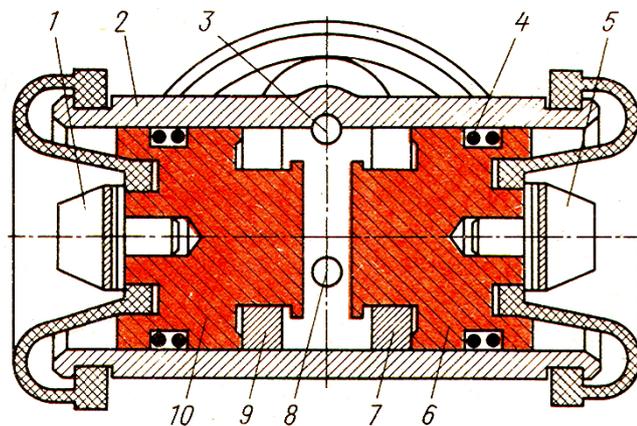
Колесный тормозной цилиндр автомобиля ГАЗ-24 «Волга»: 1, 5 – толкатели; 2 – корпус; 3 – верхнее отверстие; 4 – манжеты; 6, 10 – поршни; 7, 9 – кольца; 8 – нижнее отверстие.
